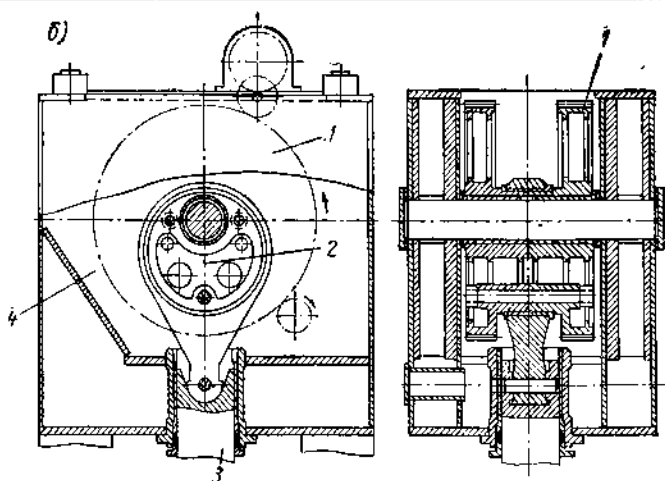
Двухстоечный кривошипный пресс с закрытой станиной и закрытым приводом
